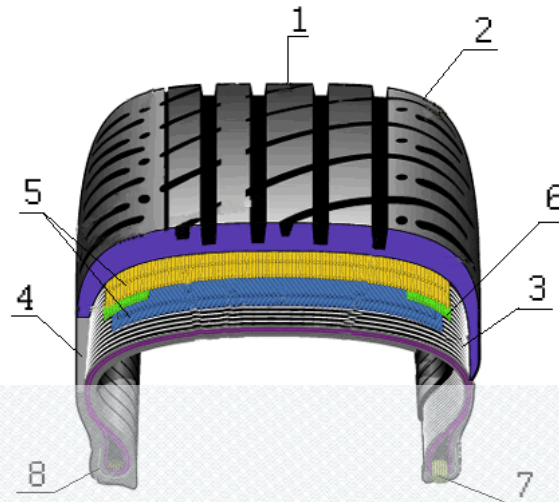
Конструкція пневматичної шини: 1 — протектор; 2 — плечовий блок з ламелями; 3 — каркас; 4 — боковина; 5 і 6 — бреккер; 7 — бортове кільце; 8 — борт шини
